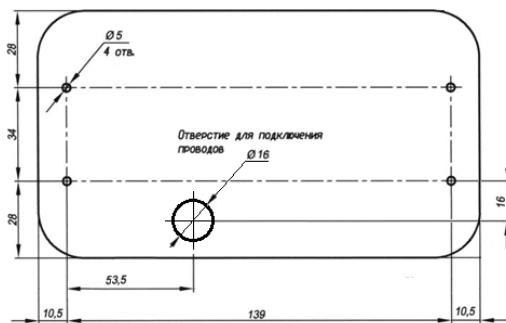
Присоединительные размеры корпуса и крепежных отверстий относительно выхода скрытой проводки
